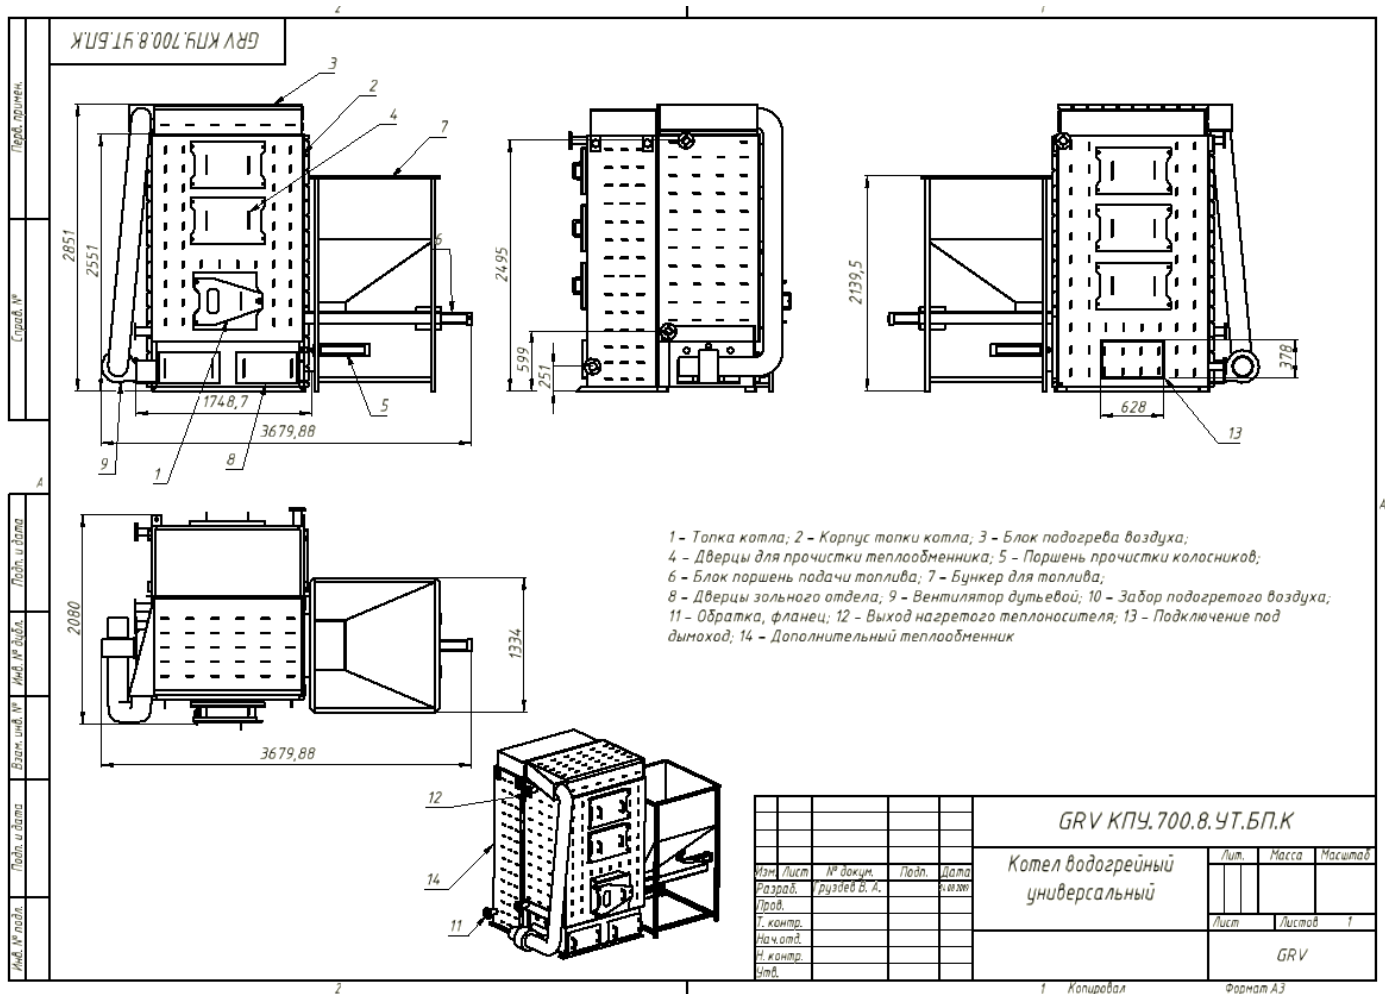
Чертеж котла. 1 – Топка котла; 2 – Корпус топки котла; 3 – Блок подогрева воздуха; 4 – Дверцы для прочистки теплообменника; 5 – Поршень прочистки колосников; 6 – Блок поршень подачи топлива; 7 – Бункер для топлива; 8 – Дверцы зольного отдела; 9 – Вентилятор дутьевой; 10 – Забор подогретого воздуха; 11 – Обратка, фланец; 12 – Выход нагретого теплоносителя; 13 – Подключение под дымоход; 14 – Дополнительный теплообменник для повышения мощности котла.
